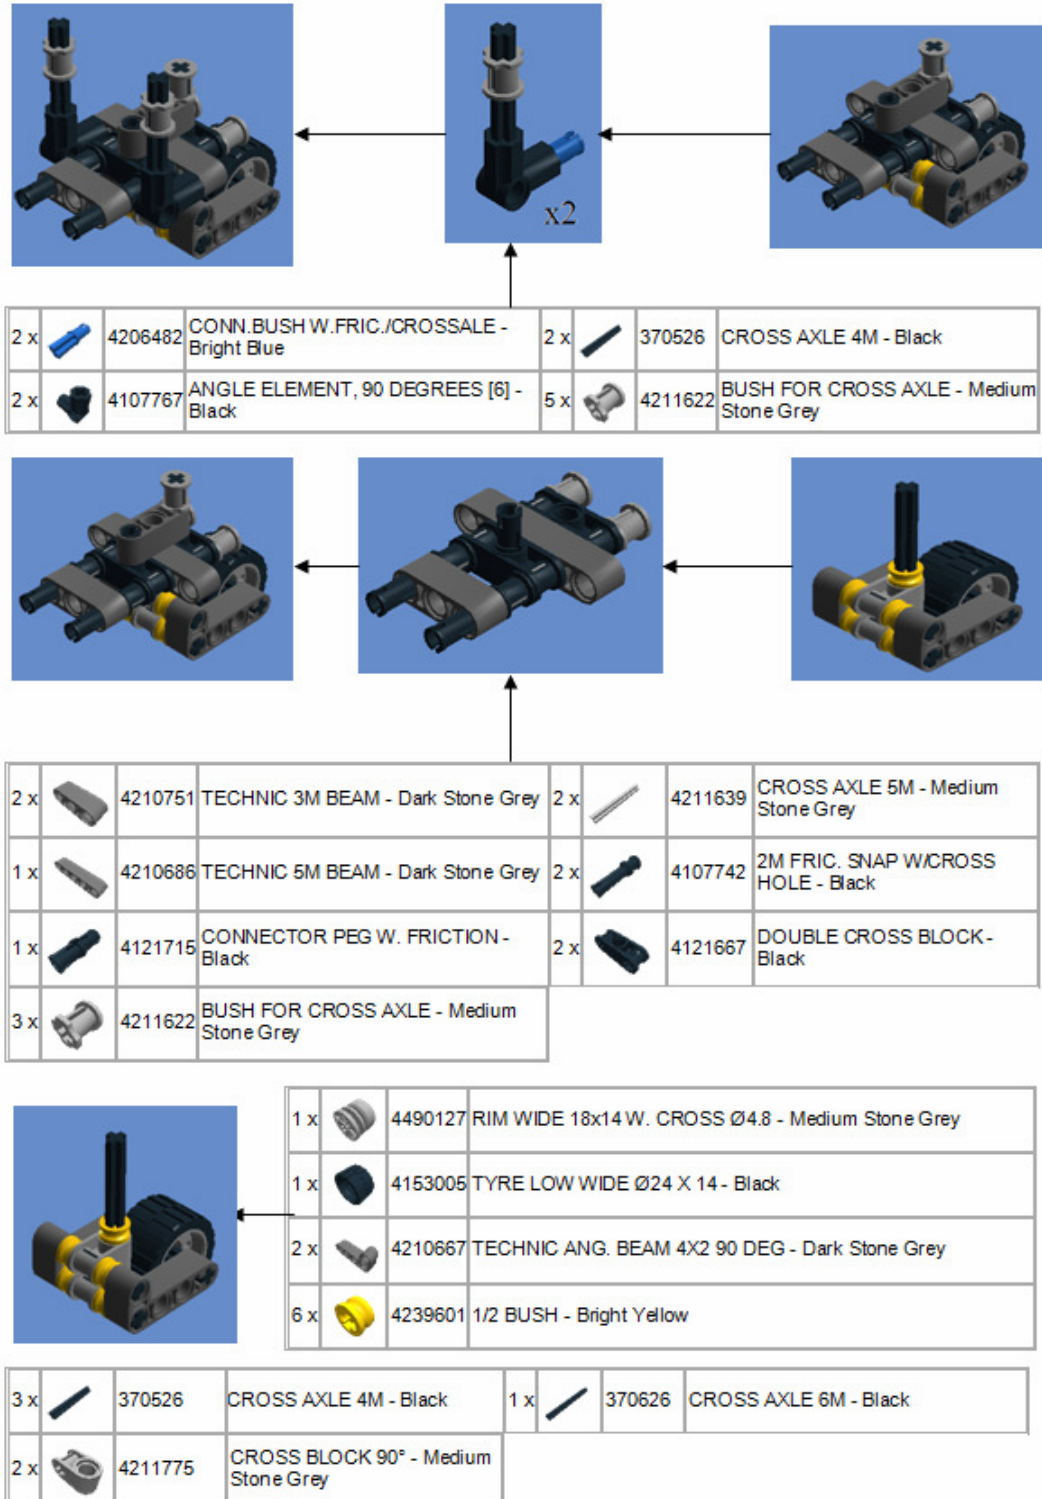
B.B2.1): Montaje de la primera parte, apoyo trasero.
